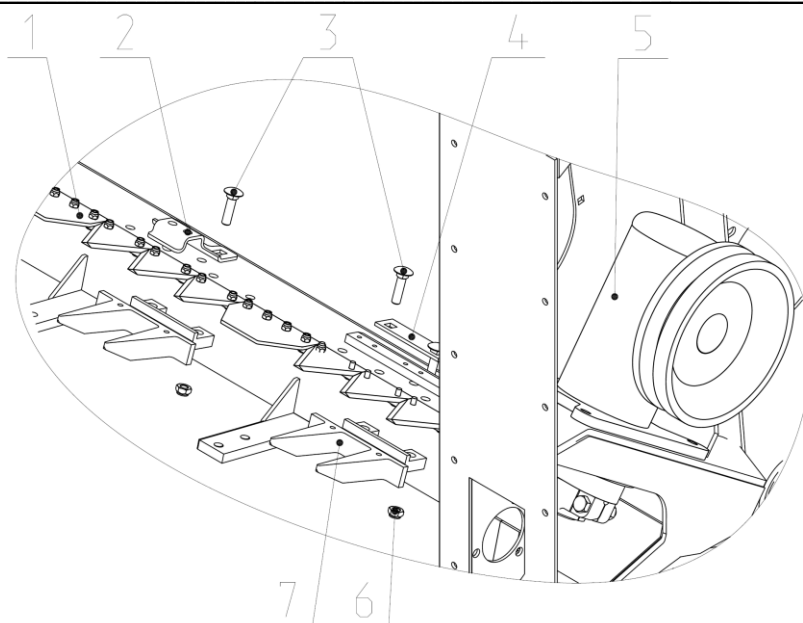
ЖНС 06.000 Режущий аппарат в сборе.
